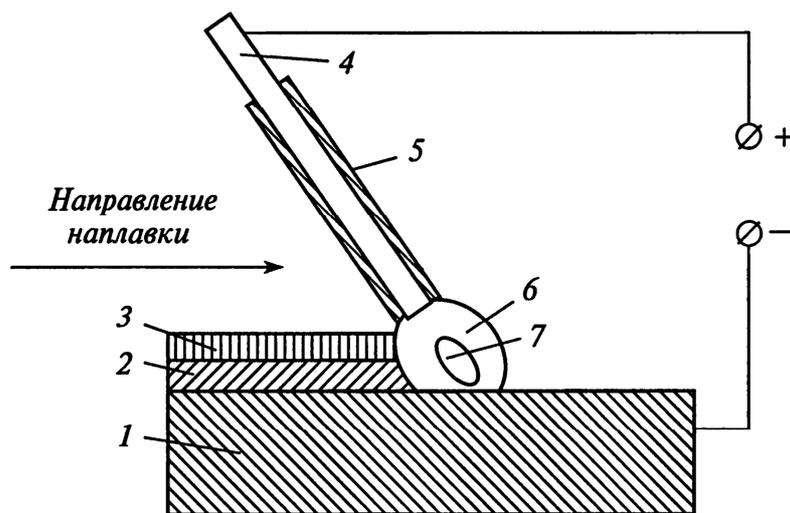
Схема ручной наплавки: 1 – основной металл; 2 – наплавленный валик; 3 – шлаковая корка; 4 – электродный стержень; 5 – покрытие электродного стержня; 6 – газшлаковая защита; 7 – сварочная ванна
